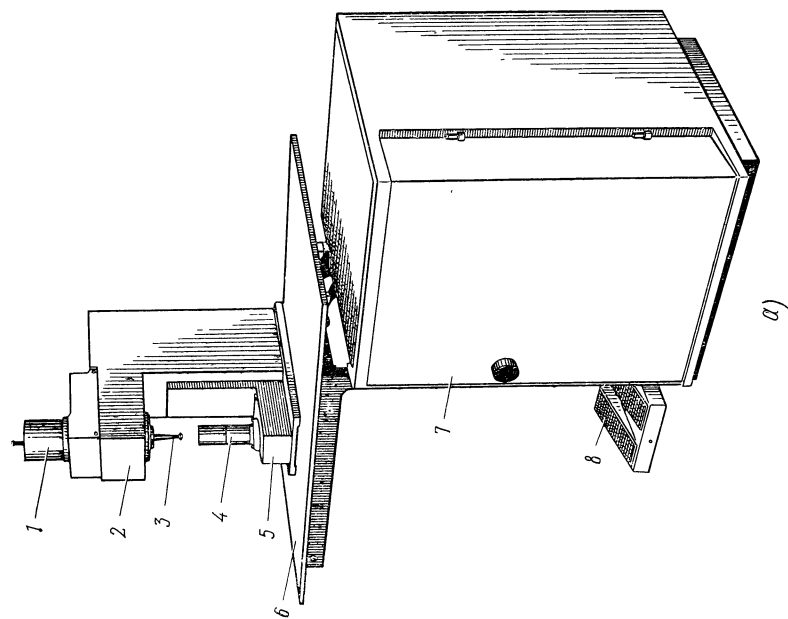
Сварочное устройство ультразвуковой машины МТУ-0,4:
